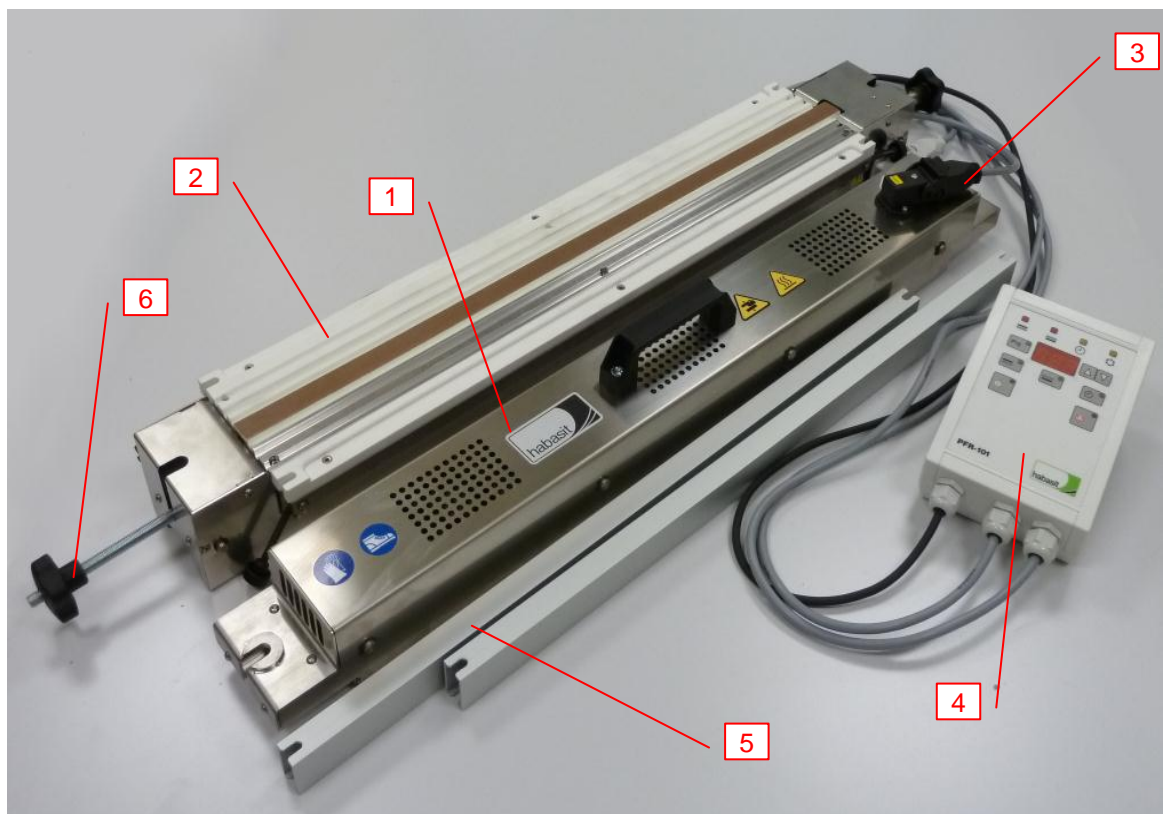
VUE D'ENSEMBLE DE LA PRESSE MODELE PQ-603
